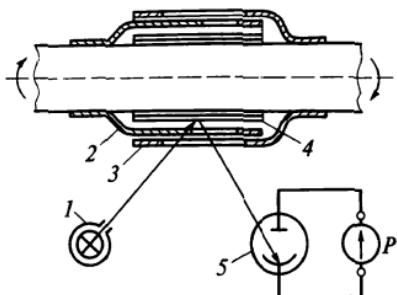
Схема цепи и конструкция фотоэлектрического преобразователя для измерения крутящего момента:
